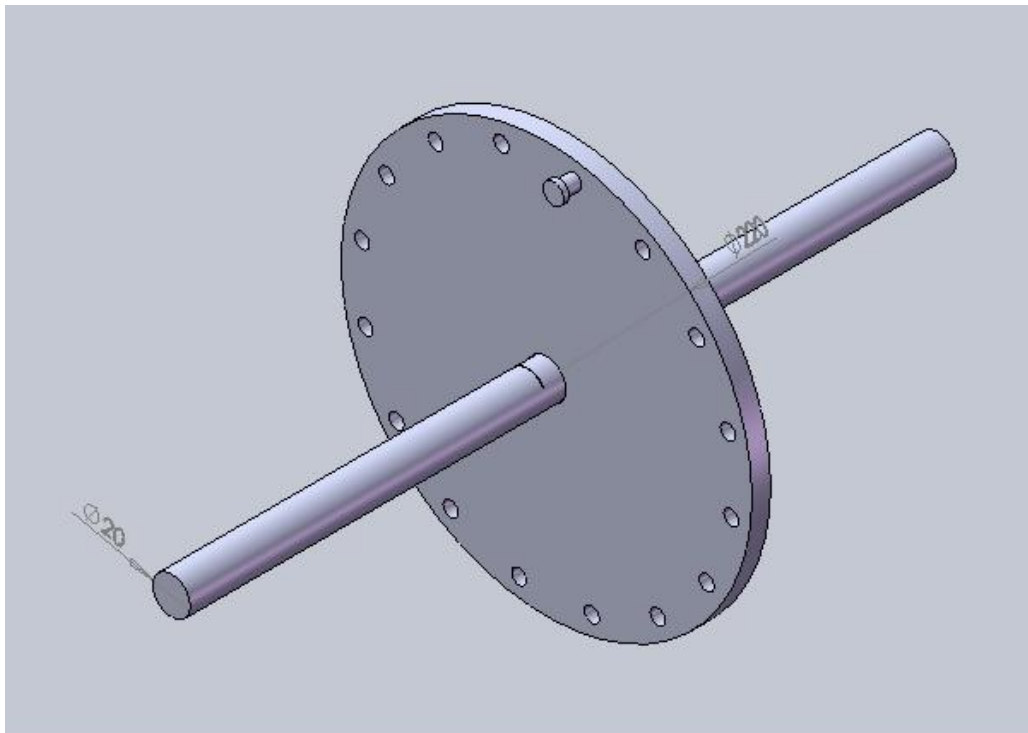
Montagem do eixo com volante desbalanceado a “0°”
